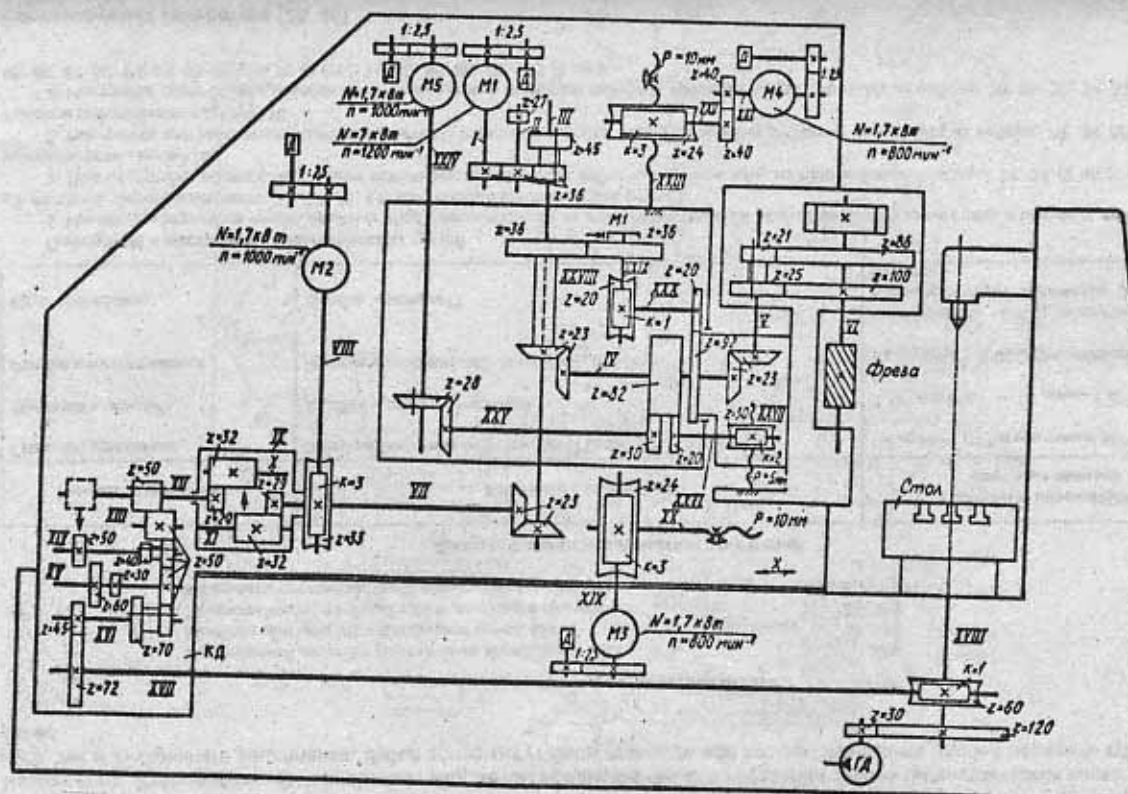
Кинематическая схема зубофрезерного полуавтомата мод. 53А20Ф4 с ЧПУ
